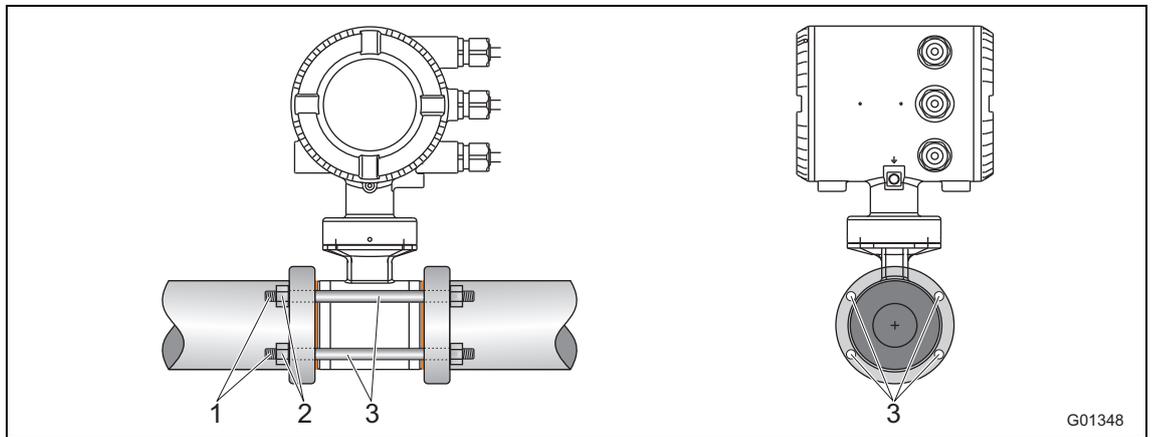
Set de montaje para dispositivos con diseño Wafer
